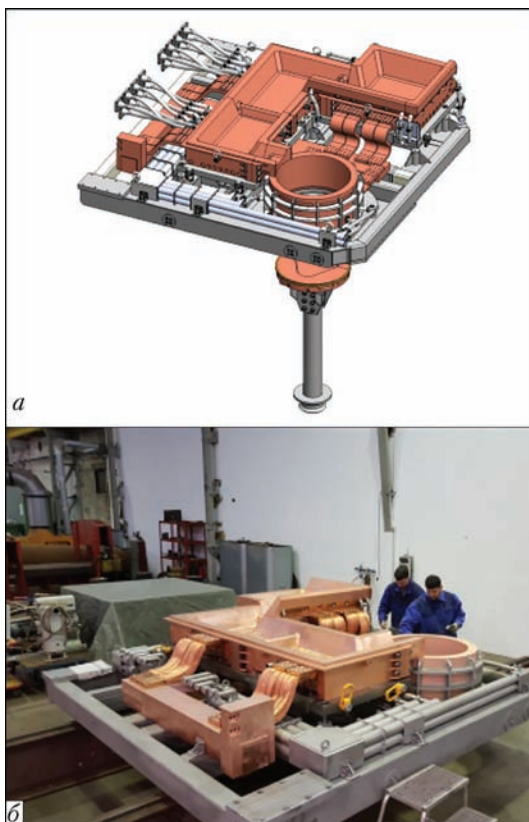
Конструкция кристаллизатора с холодным подом для ПД печей: а — схема; б — внешний вид
